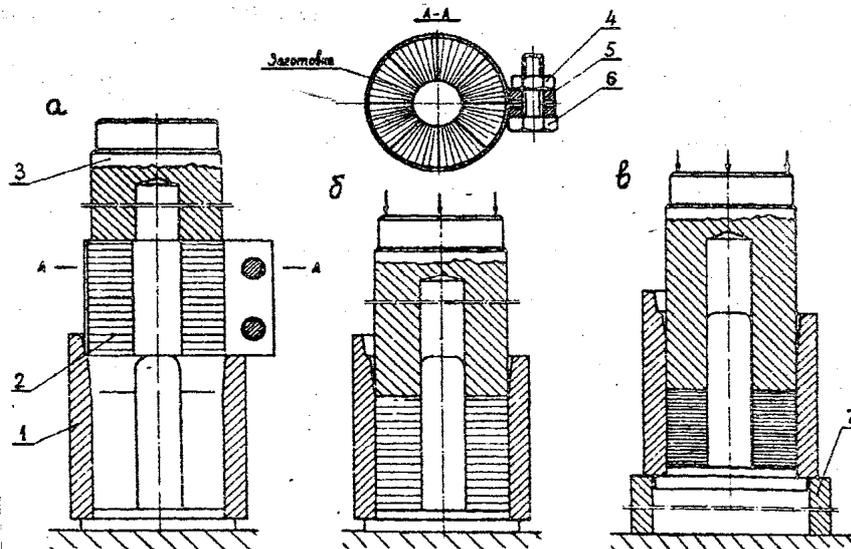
Технология сборки втулки из секторов прессованной древесины:
